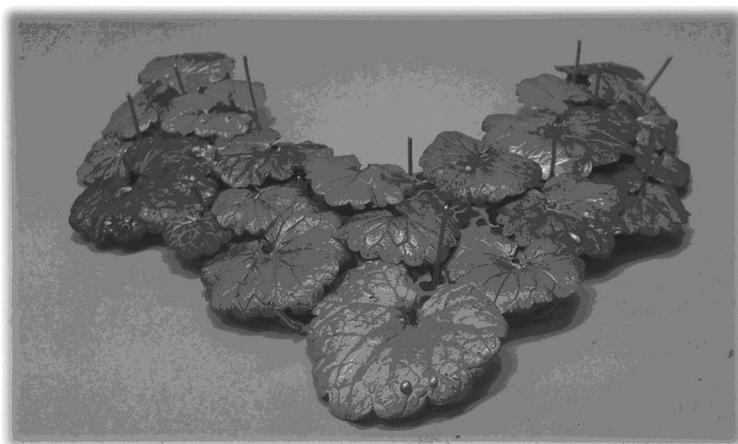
Обработка изделия + пайка штифтов под закрепку
